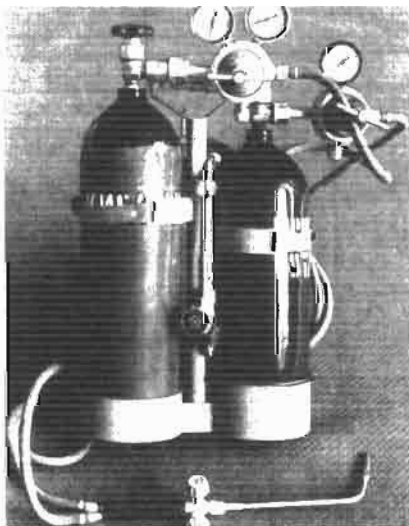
Переносная установка ПГУ-3-02 для ручной сварки, пайки и резки
